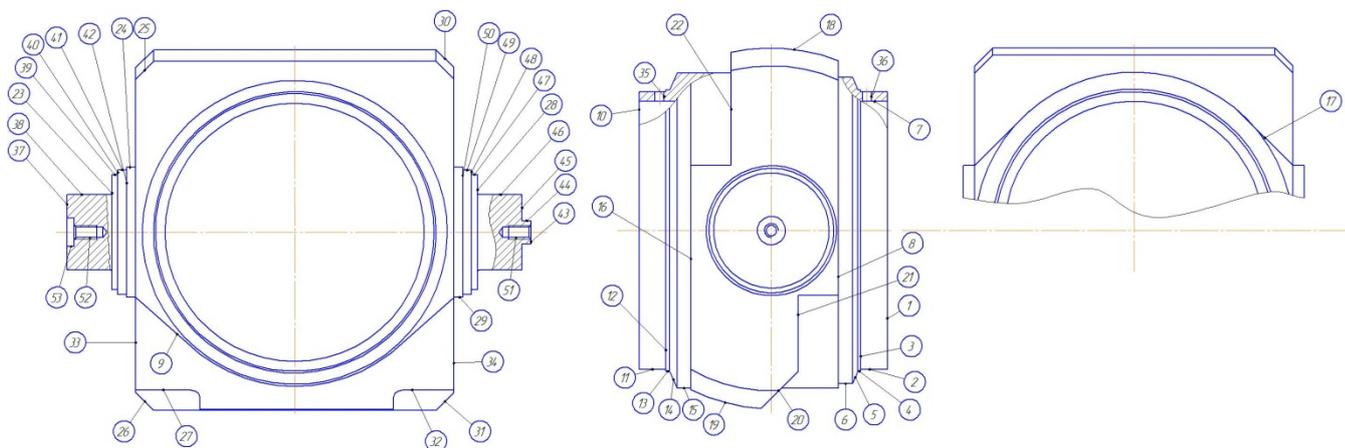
Эскиз детали с номерами обрабатываемых поверхностей
